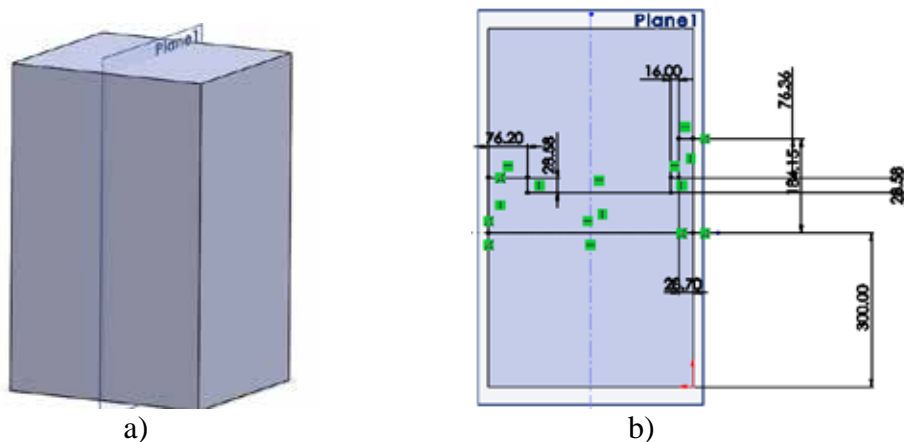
Plano 1 y Croquis 2, Cámara de flujo.
